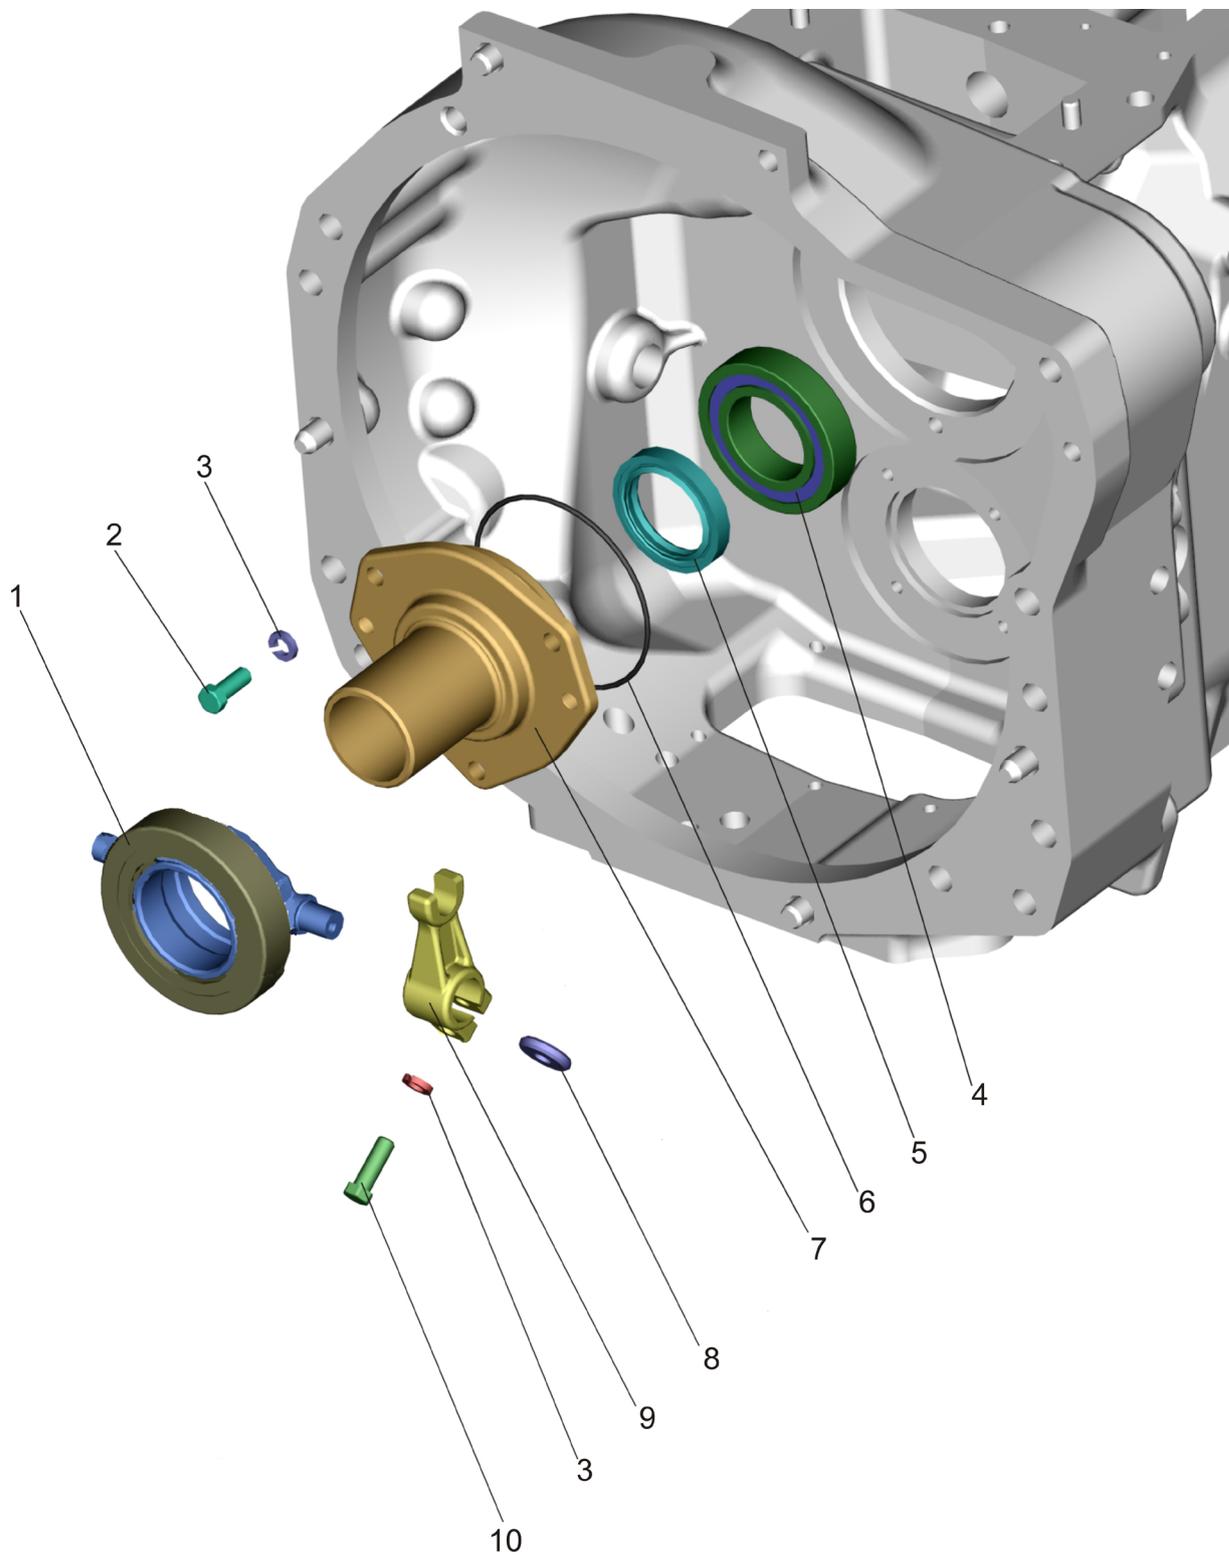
Корпус сцепления. Отводка (с установкой муфты LuK)
